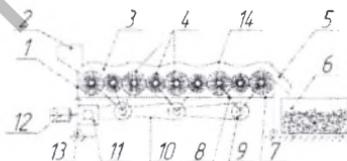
Схема устройства для очистки товарного картофеля: 1 – корпус; 2 – загрузочная воронка; 3 – рабочая камера; 4 – рабочие органы (вальцы); 5 – разгрузочная воронка; 6 – емкость; 7 – перфорированное днище; 8, 10 – цепная передача; 9 – звездочка; 11 – редуктор; 12 – электродвигатель; 13 – передвижные опоры; 14 – прорезиненное полотно
